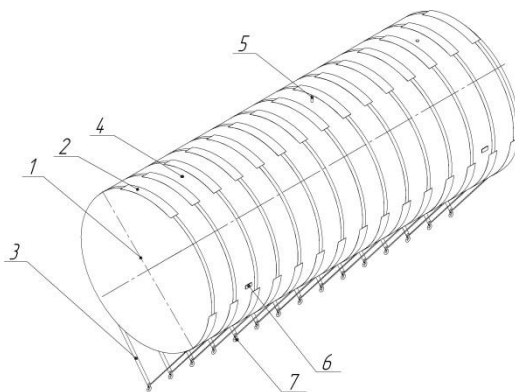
1 - Полимерная герметичная оболочка цилиндрической формы; 2 - Защитная полоса; 3 - Грузоподъемная стропа; 4 - Воздушный клапан; 5 - Предохранительный клапан; 6 - Ручка резиновая; 7 - Чалочный крюк.
